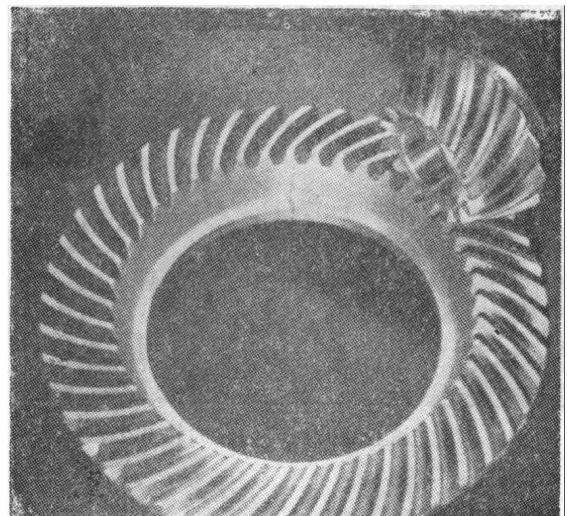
范成加工的弧齿锥齿轮的大轮和小轮
